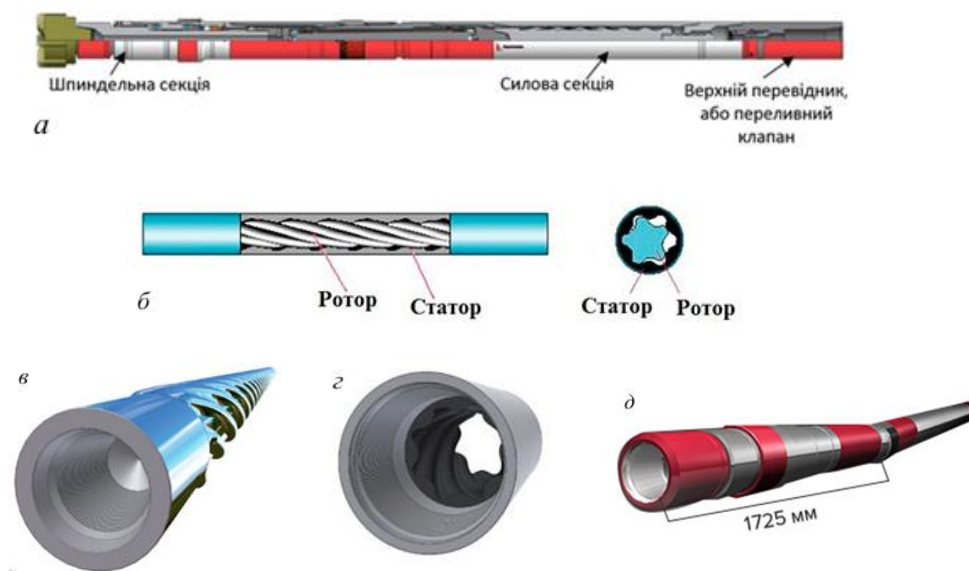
Типова конструкція гвинтового вибійного двигуна:
